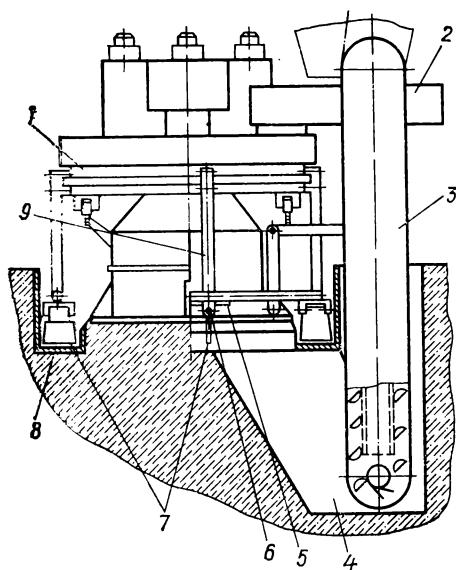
Приставка для механизированной уборки просыпли смеси из-под стола пресса:
